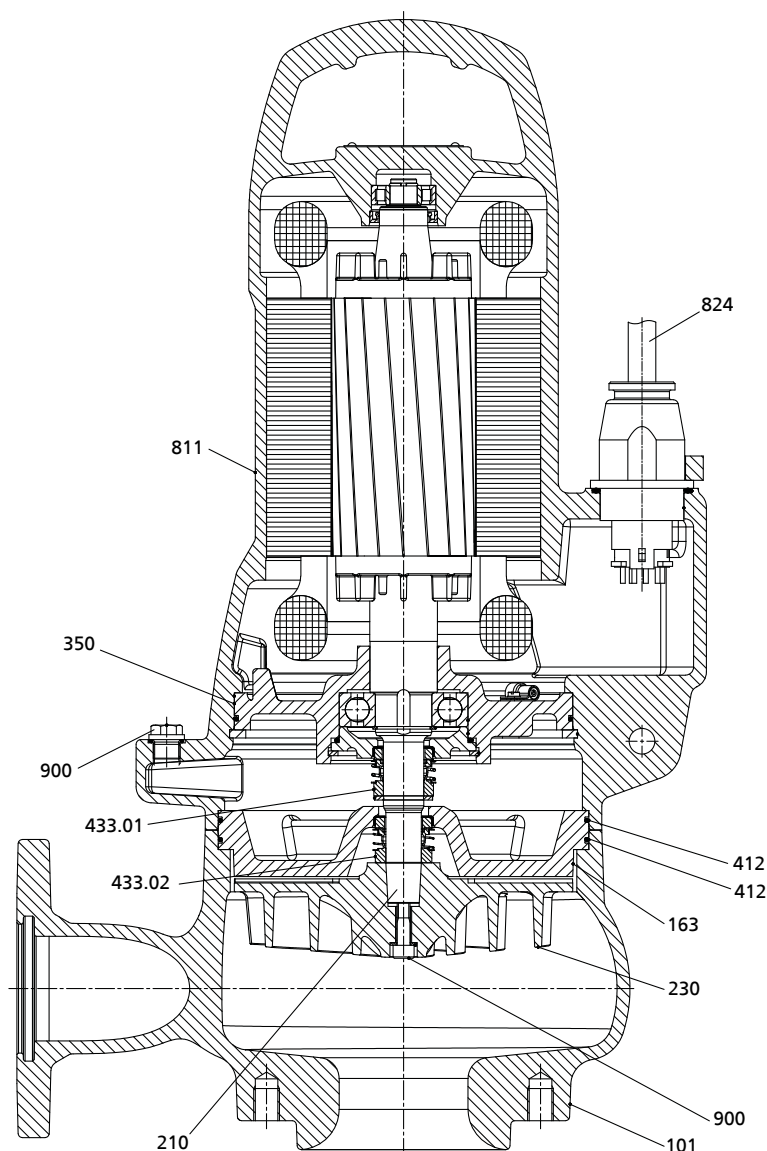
Сборочный чертеж, пример: Amarex KRT F65-215
